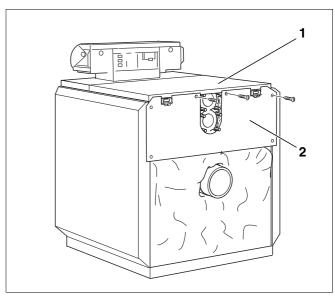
Montage – panneau arrière supérieur de la chaudière
